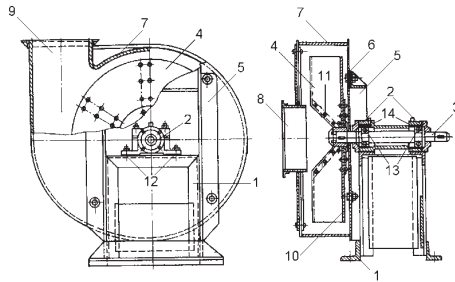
Общий вид малошумного вентилятора; рис.2 – его профильная проекция в разрезе: 1 - рама, 2 - опоры, 3 - вал, 4 - сборное рабочее колесо, 5 - каркас из уголков, 6 - упругие прокладки между корпусом вентилятора 7 и патрубками, 7 - корпус вентилятора, 8 - входной патрубок, 9 - выходной патрубок, 10 - диск, 11 - лопатки рабочего колеса, 12 - упругие прокладки для установки корпуса опор 2 вала 3 на раме 1, 13 - подшипники вала 3, установленные в корпусе опор 2 посредством упругих втулок 14.
